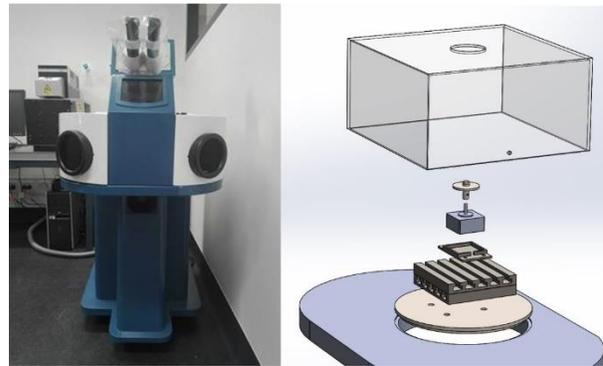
Links - Schweiß-Laser; Rechts - Design für Stepper-Motor-Vorrichtung in Maschinenkammer.
